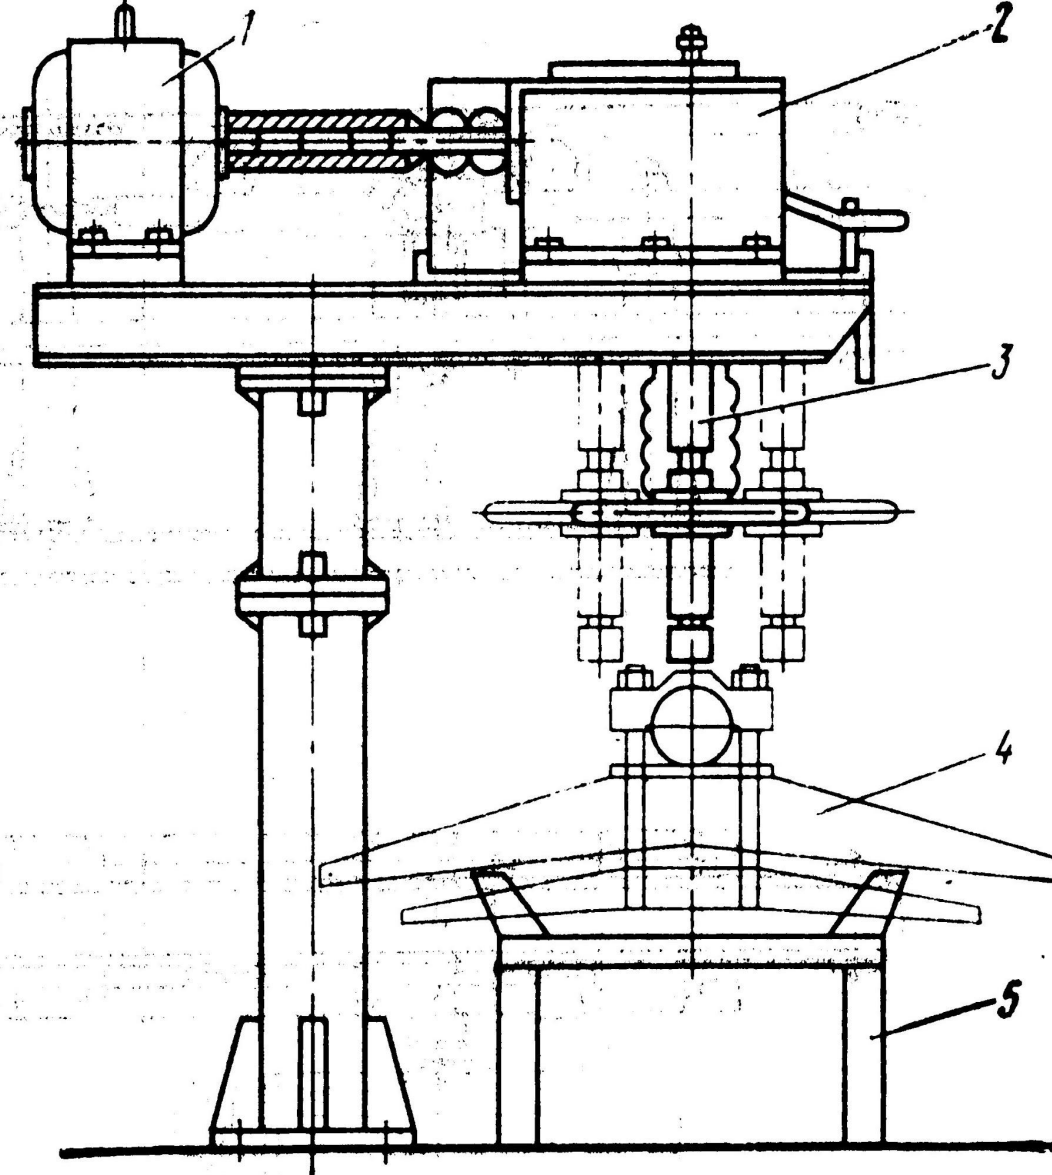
Станок для отвертывания гаек крепления стремянок рессор:
